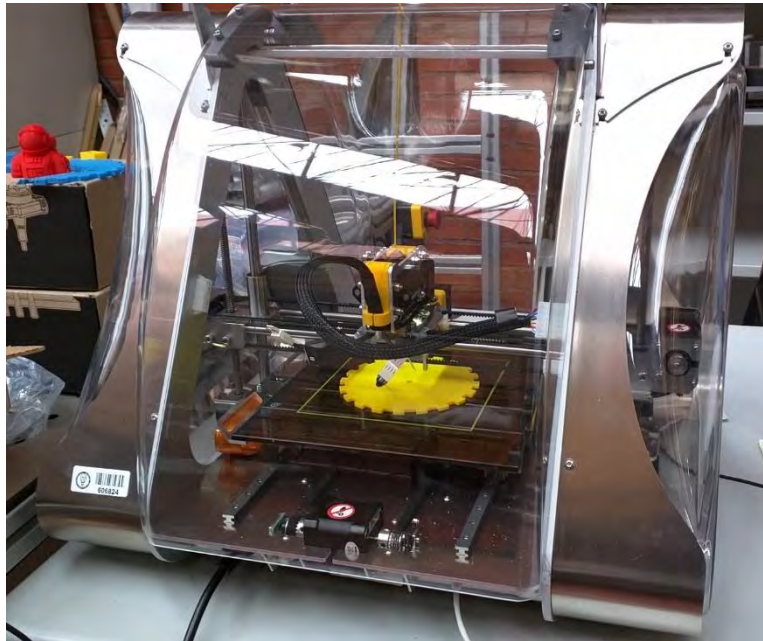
ZMorph 2.0 SX imprimiendo el engranaje de un dispensador.
